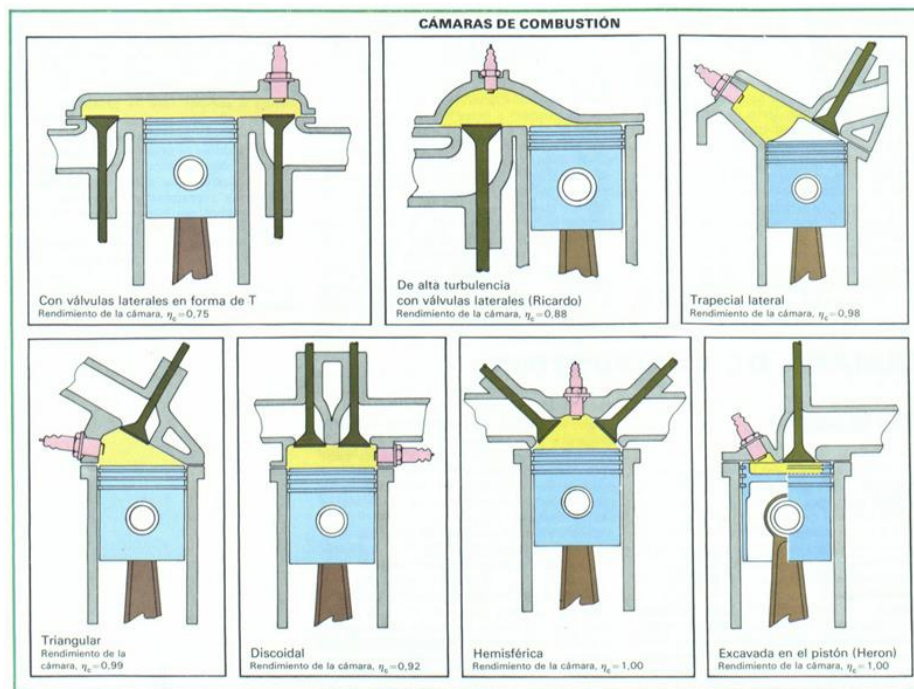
Tipos de Cámara de combustión. Fuente: Motorgiga.com [33]
